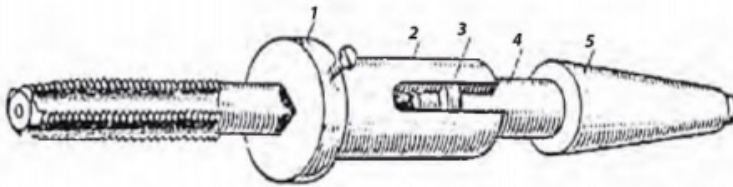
Пристосування для закріплення мітчика на токарному верстаті:
